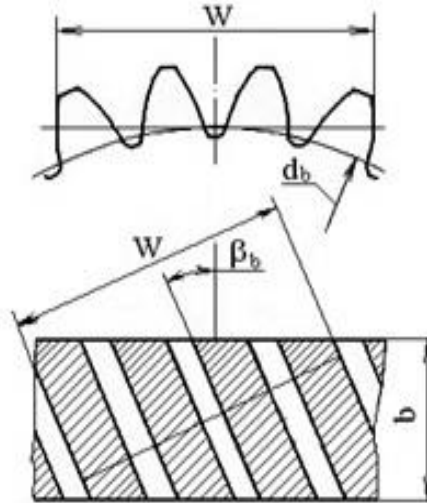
Схема замера длины общей нормали зубьев цилиндрических колес (сечение зубьев колеса плоскостью, касательной к основному цилиндру)
